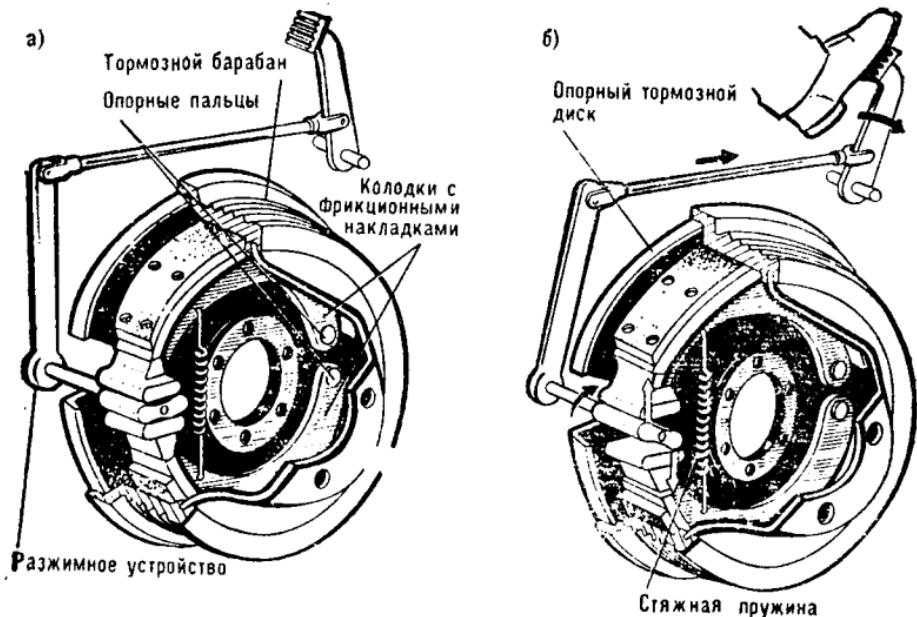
Схема работы колесного барабанного тормозного механизма:
